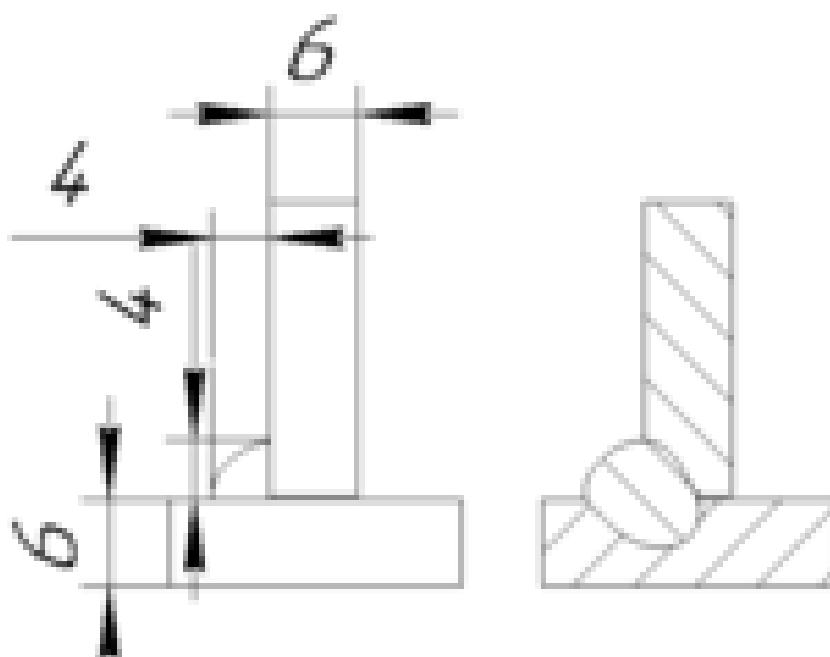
Общий вид сборки и сварки шва Т1
